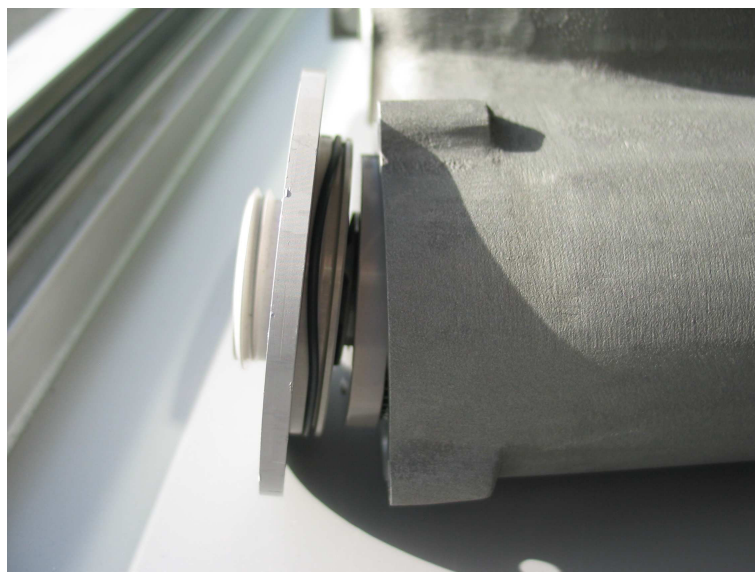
Пример установки в картер двигателя крышки фильтра с неправильным положением уплотнительного кольца.
